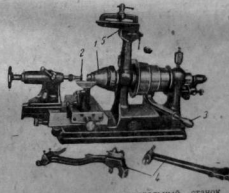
Револьверный станок Бреге для обточки корпусов.
